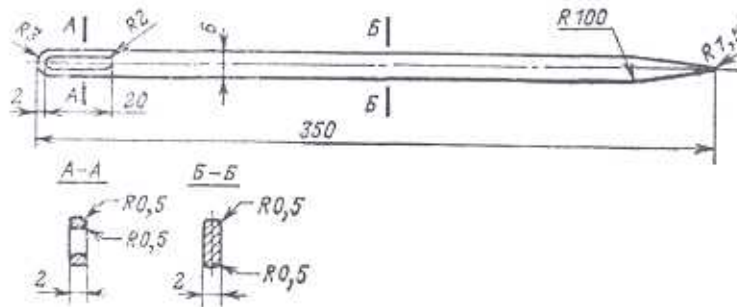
Игла для вязки бандажей лобовых частей обмотки статора
